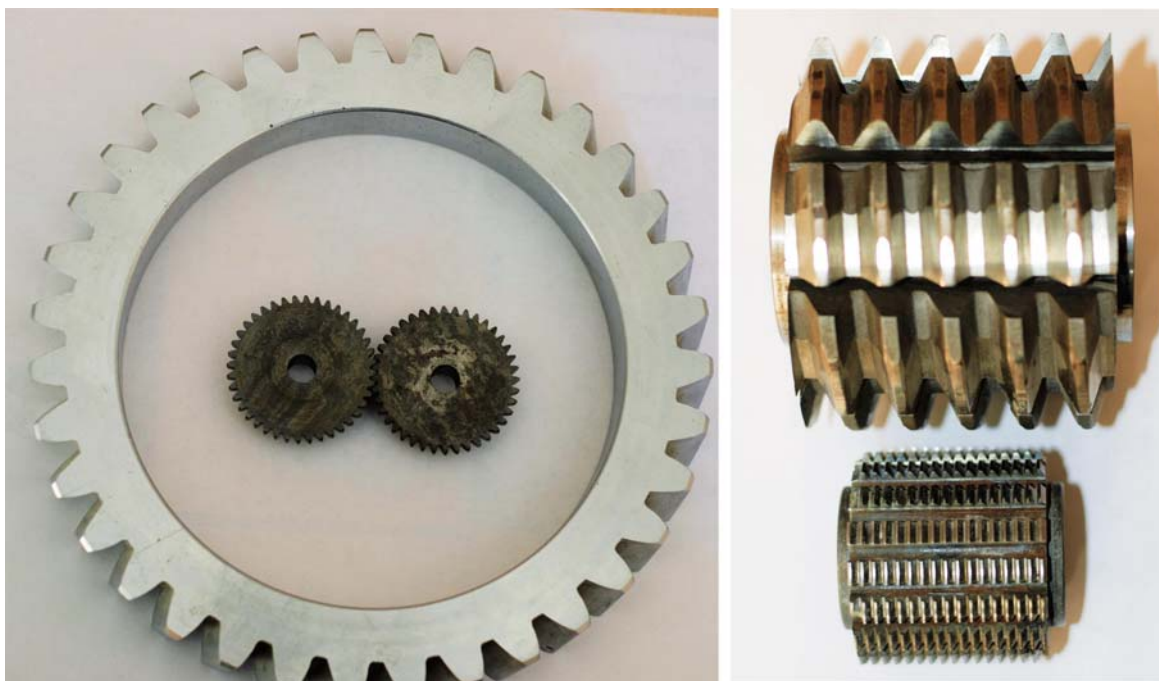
Зубчатые колеса с несимметричными профилями зубьев с модулями $m = 5$ мм, $m = 1$ мм и фрезы для нарезания этих зубьев
